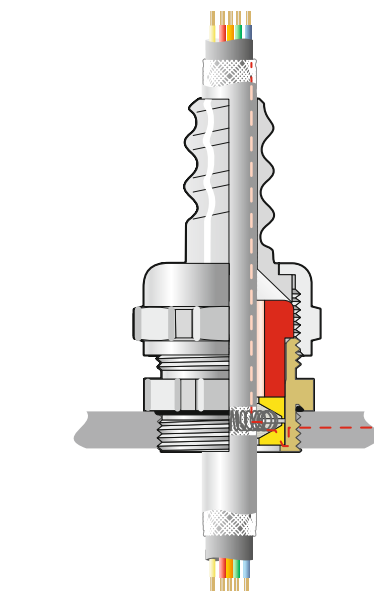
UNI HF-UL Dicht sobre cable con pantalla trenzada
